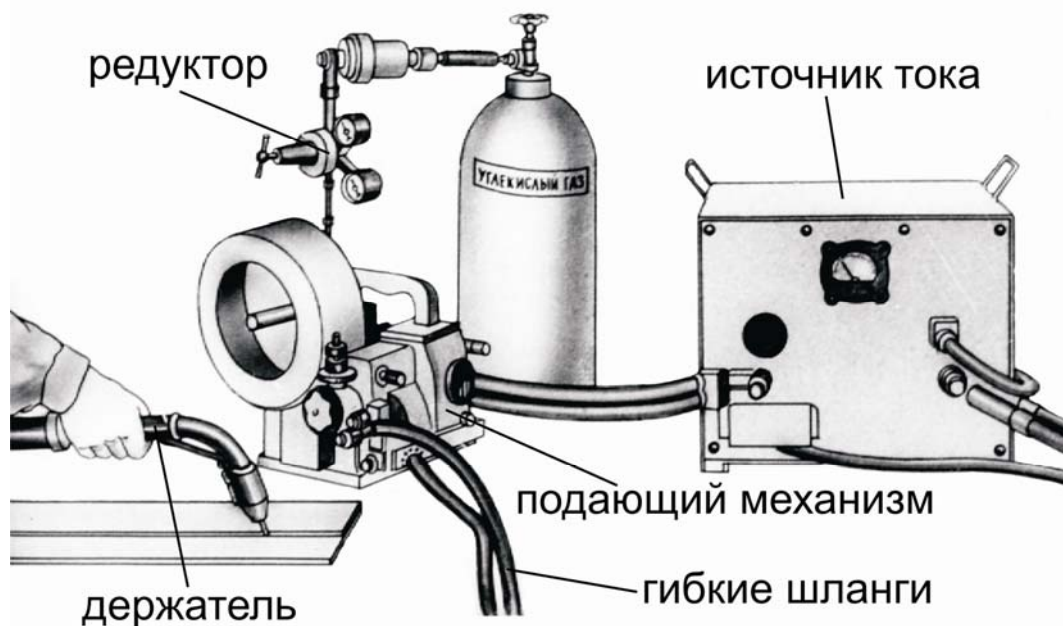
Схема установки для механизированной сварки в защитных газах
